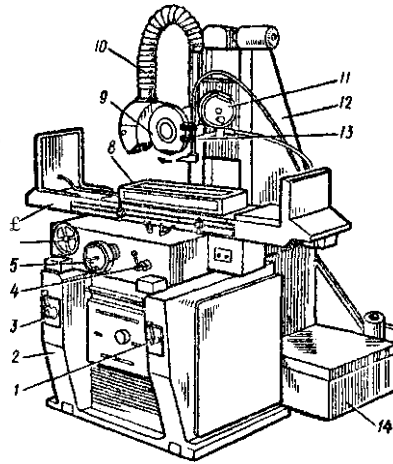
Плоскошліфувальний верстат ЗБ71М
